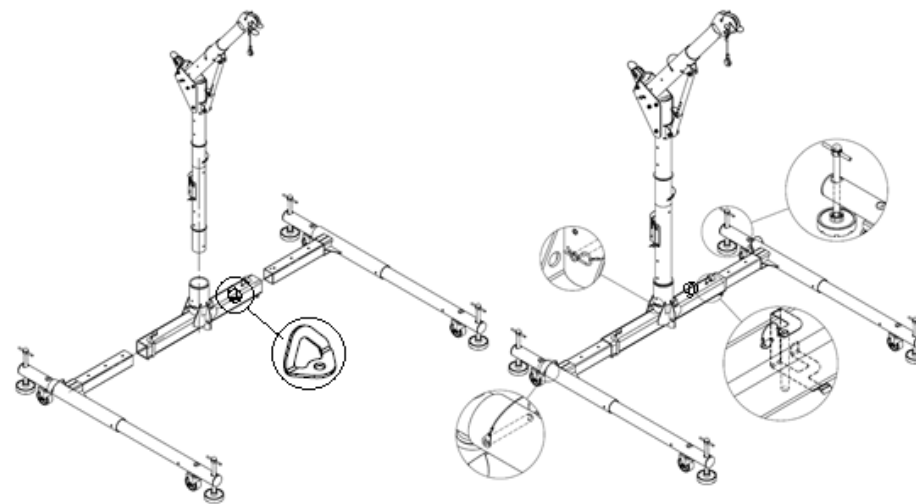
Монтаж СОБ Кран Е11-1Н
